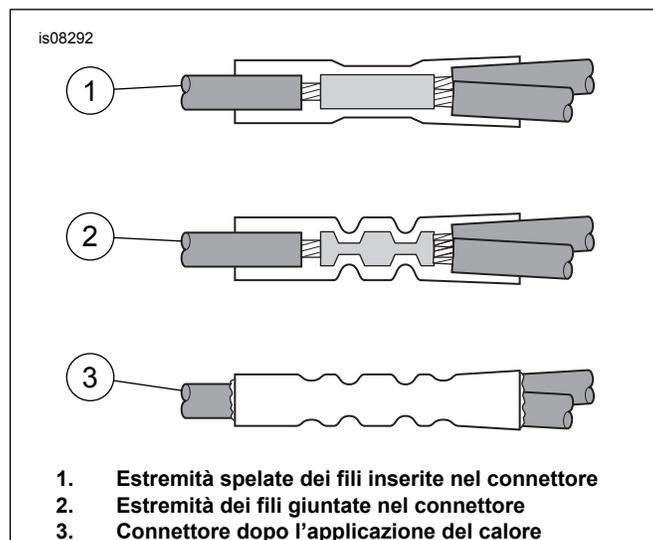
Installazione dei connettori a giunto di testa a tenuta
